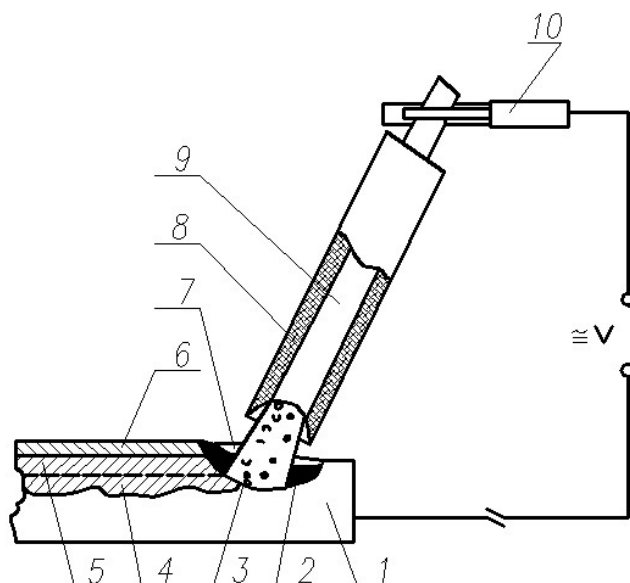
Схема ручной дуговой сварки штучным электродом:
